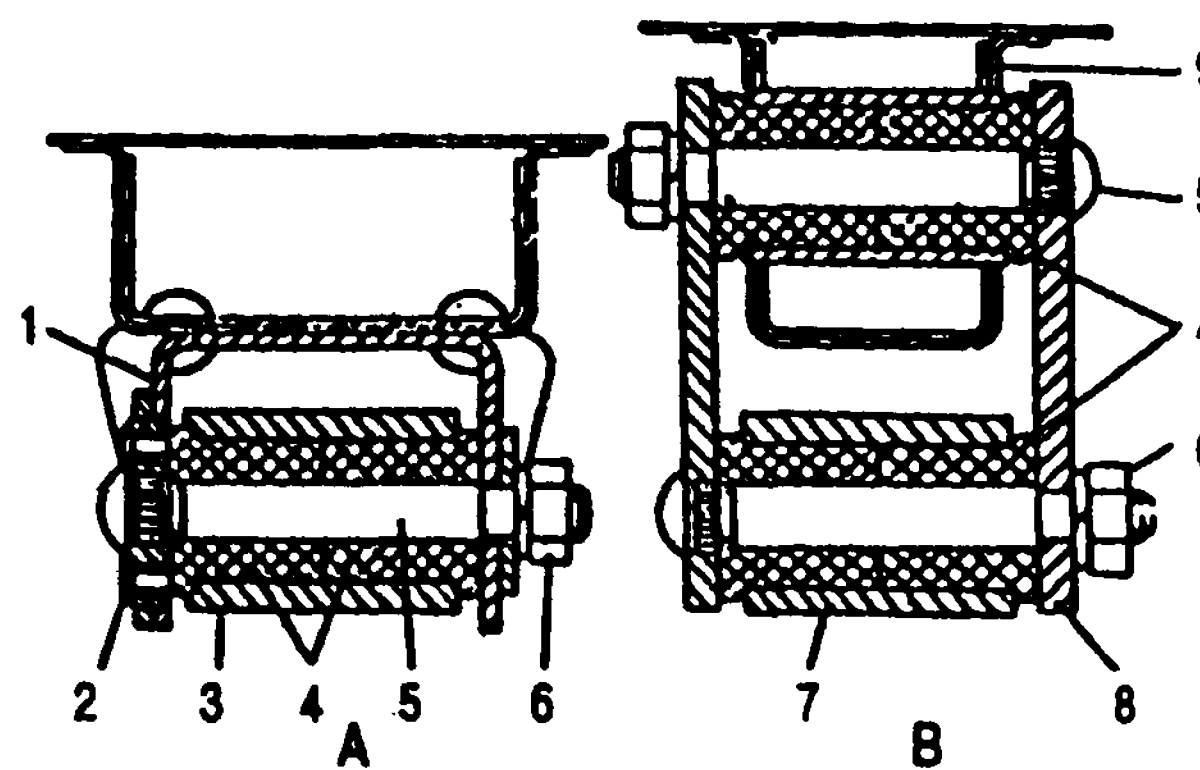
Крепление концов рессоры: 1 - кронштейн; 2 - шайбы; 3 - переднее ушко рессоры; 4 - резиновые втулки; 5 - палец; 6 - гайка; 7 - заднее ушко рессоры; 8 - щека серги; 9 - лонжерон пола кузова; А - крепление переднего конца; В - крепление заднего конца рессоры
